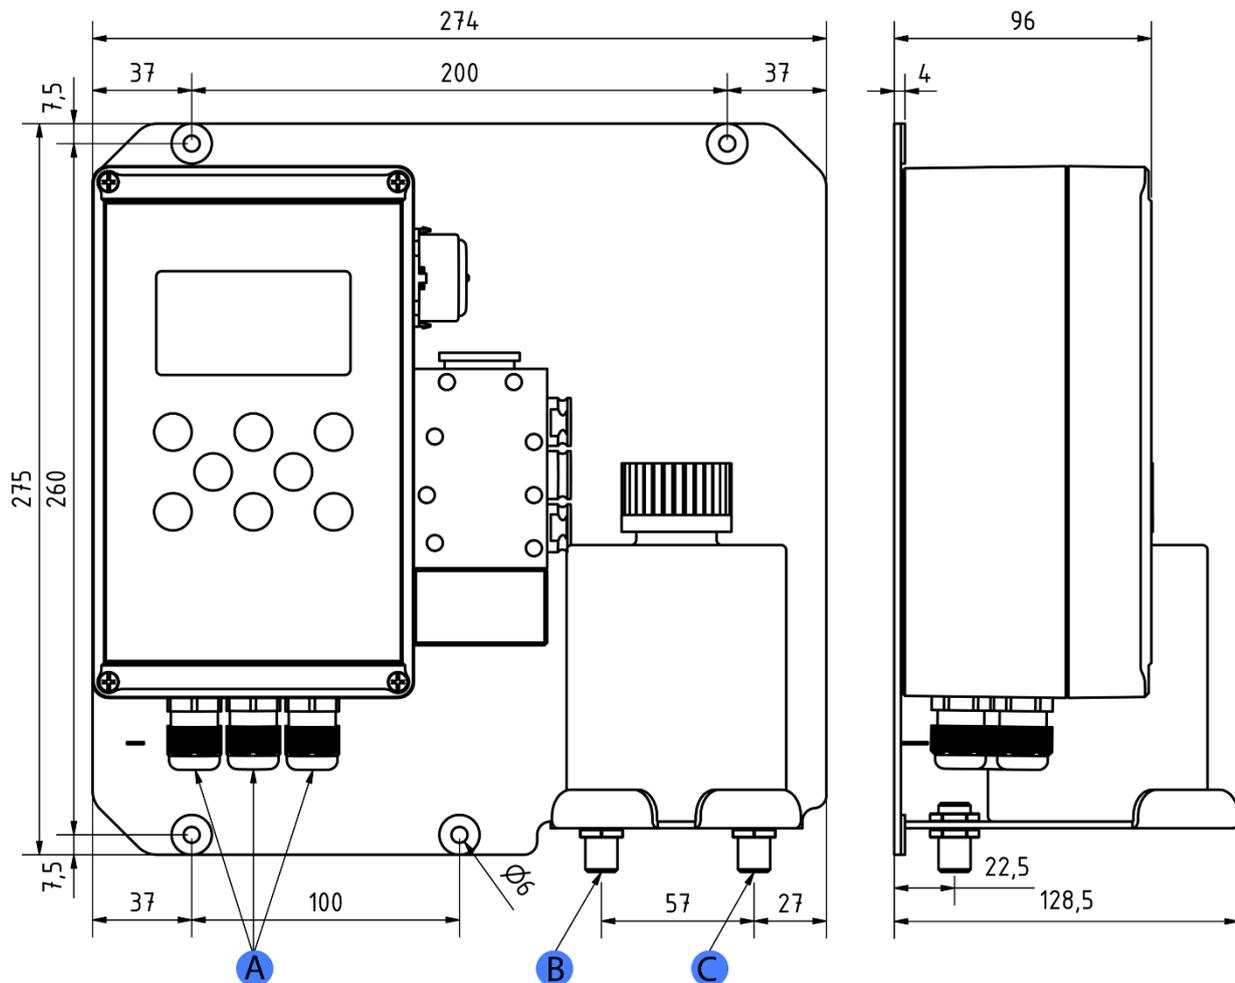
Bohrplan zur Befestigung des Analysegerätes ohne Gehäuse
